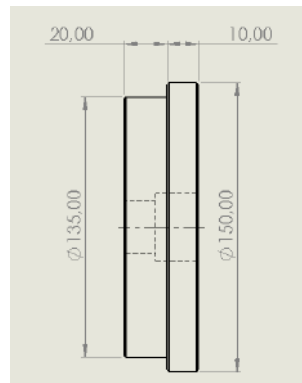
Dudukan *bearing* dengan rol *conveyor
